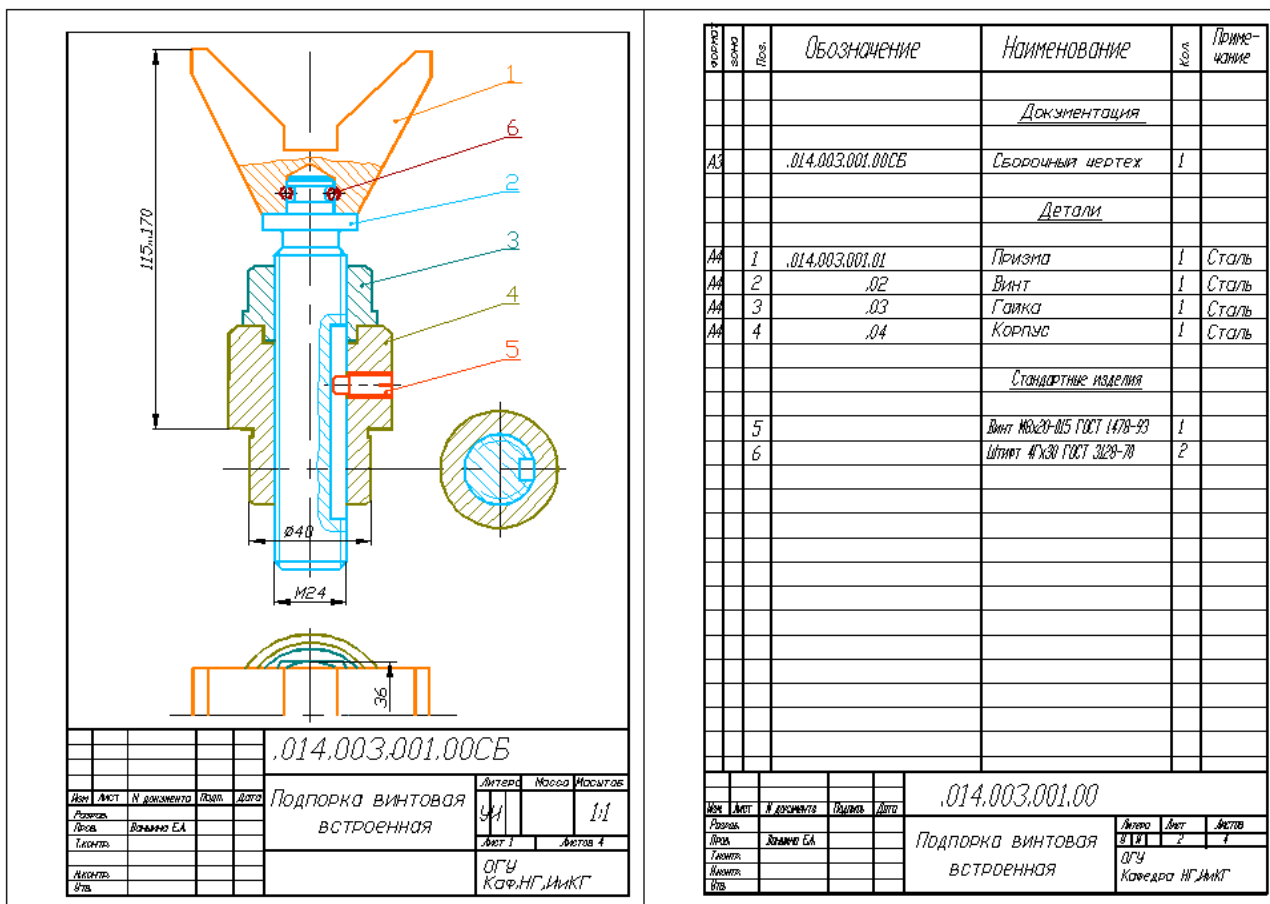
Сборочный чертеж «Подпорка винтовая встроенная».
